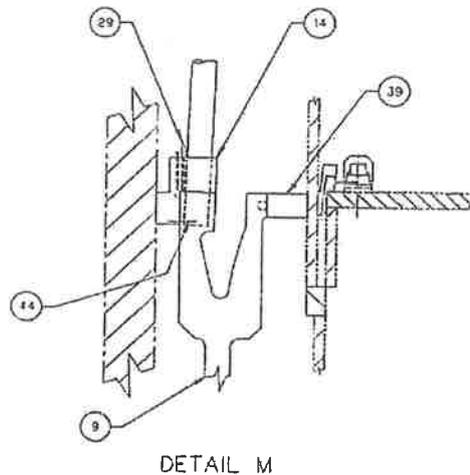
Oberer Kopf der unteren Feder mit Einschraubung der Zugstange und Passstücken
